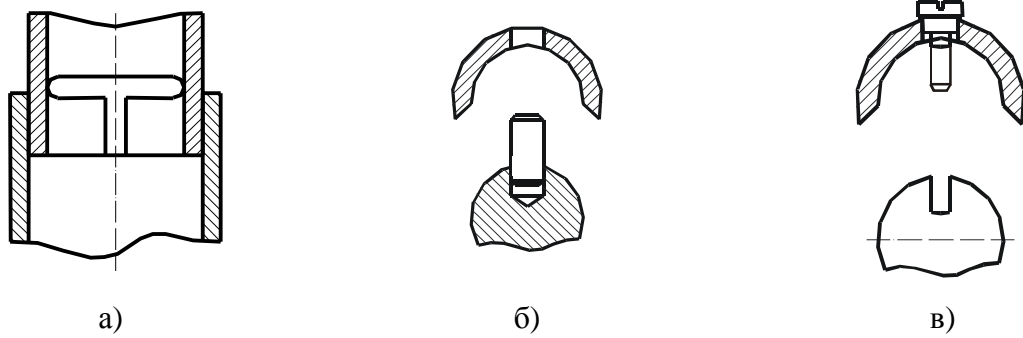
Напрявні для прямолінійного руху: а – «Г» – образний розрізі невеликорозгинання усередину трубки забезпечує вибірку зазору; застосовується в невідповідальних напрямних; б – циліндричні напрямні із запобіганням повороту за допомогою штифта; штифт встановлюється у внутрішню деталь; в – запобігання від повороту за допомогою гвинта, що має спеціальний виступ
